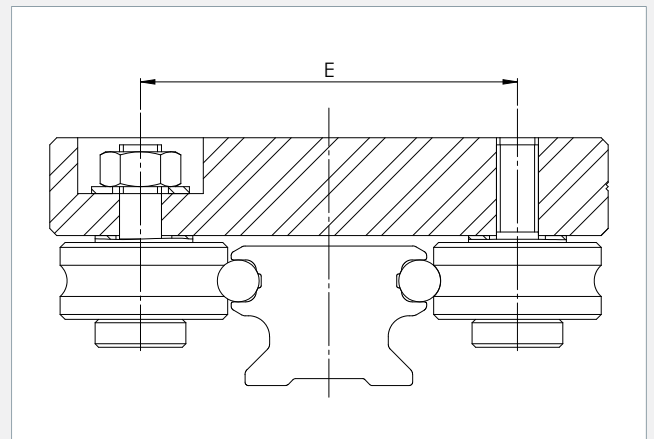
Empfohlener Laufrollenabstand / Track roller spacing
